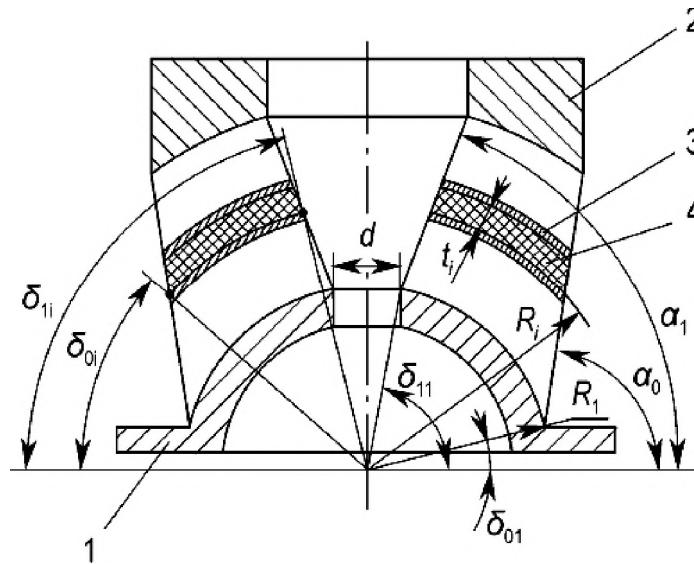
Конструкция и геометрические параметры сферического эластомерного подшипника [27]: 1 – внутренний фланец; 2 – наружный фланец; 3 – металлическая арматура; 4 – резиновые слои.
